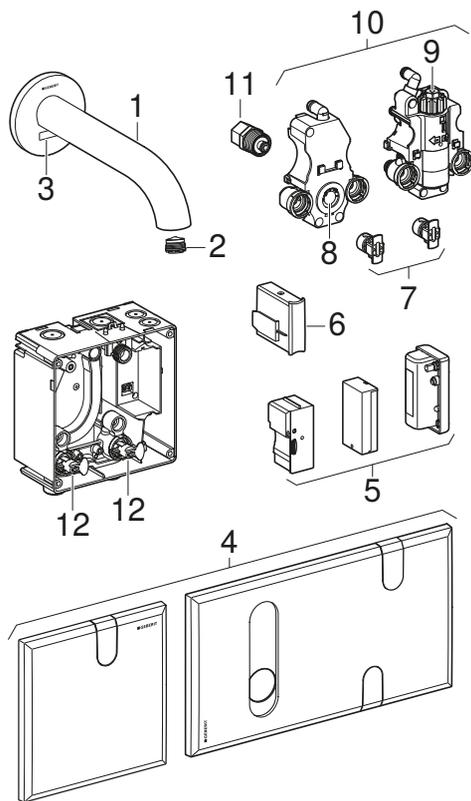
Robinetteries de lavabo Geberit Piave et Brenta, montage mural
